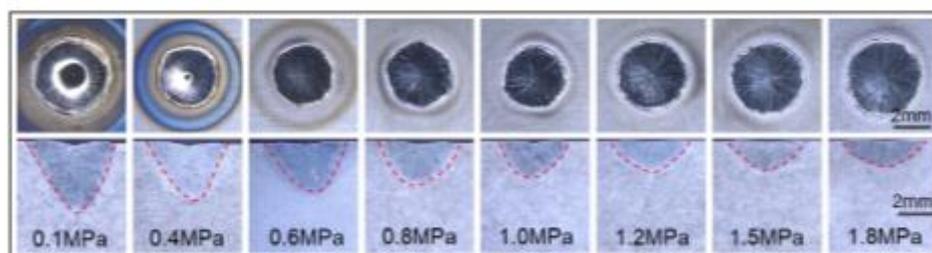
Поверхность шва и его поперечное сечение [6]
